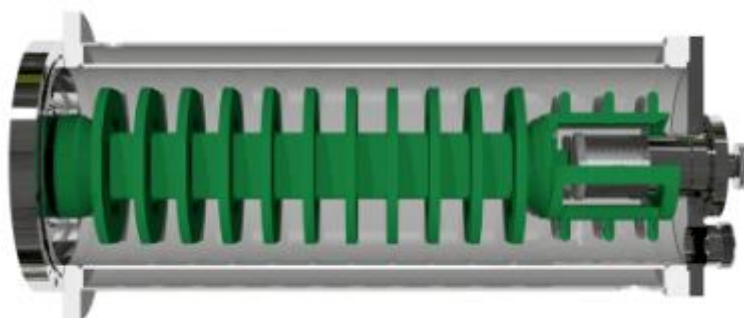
Вертикальний бісерний млин Discus Intensive Rotor
